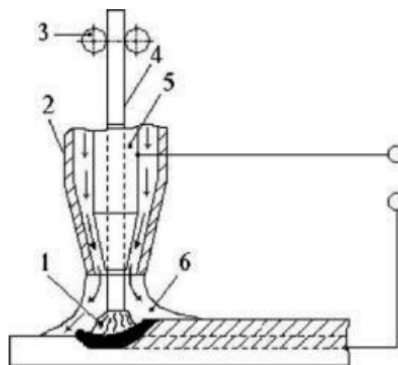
Схема зварювання в середовищі вуглекислого газу: 1 – електрична дуга; 2 – газове сопло; 3 – подавальні ролики; 4 – електродний дріт; 5 – струмopідвідний мундштук; 6 – вуглекислий газ.
